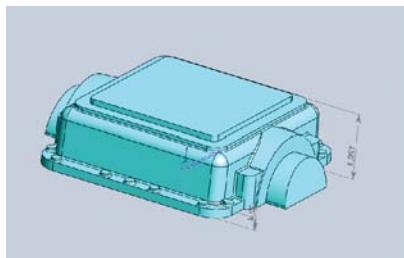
Мастер-модель «Нижняя половина корпуса редуктора»
